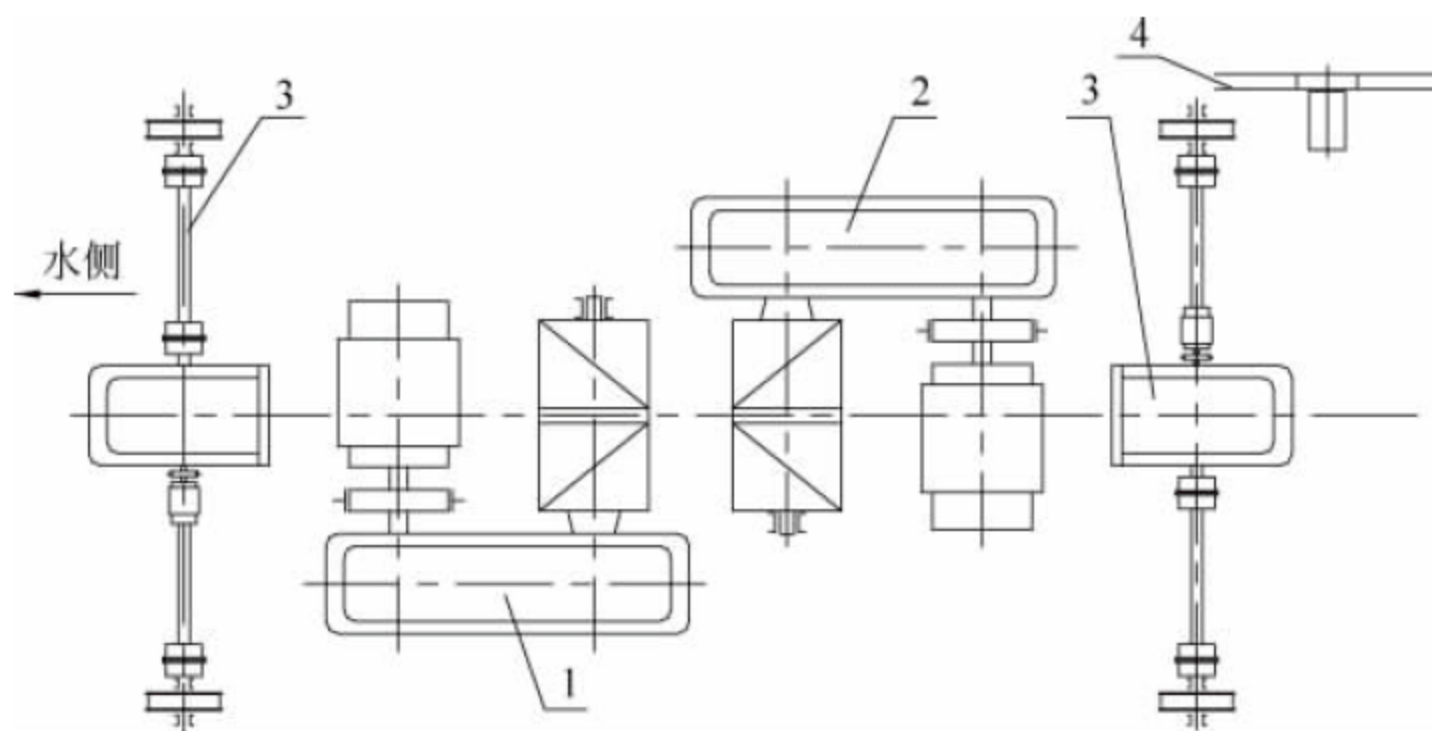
起升、开闭、小车运行和电缆卷放机构平面布置示意图
